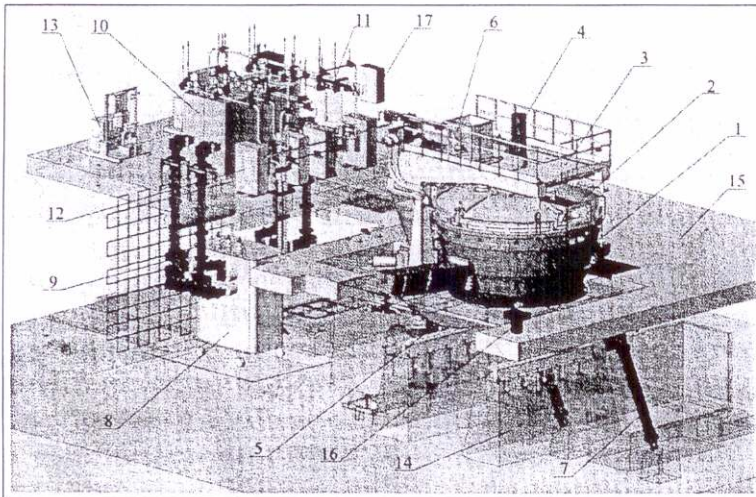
Общий вид и компоновка оборудования дуговой печи постоянного тока:
